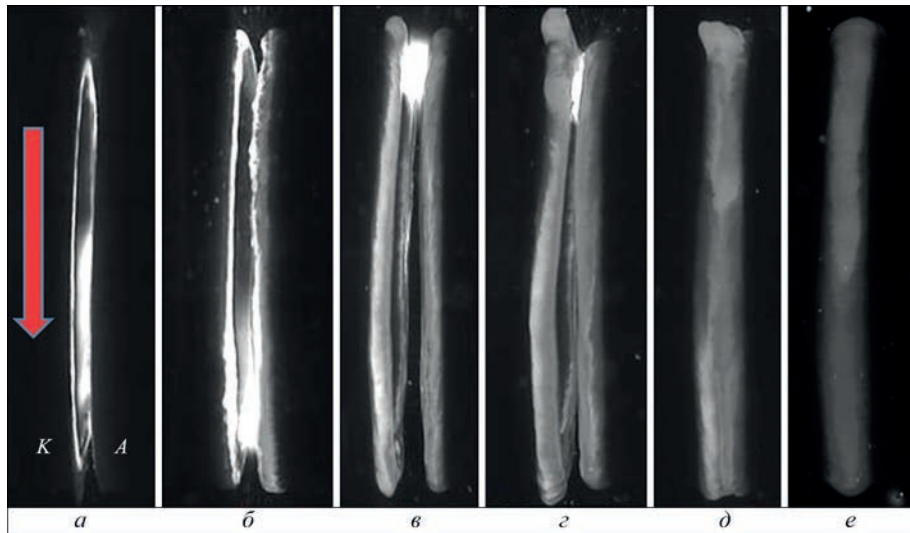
Стадії зварювання труб: а – початок переміщення дуги під дією КМП; б – формування шару розплаву на торцях труб; в – переміщення розплаву в процесі нагрівання; г – оновлення розплаву перед осадкою; д – початок осадки; е – формування зварного з'єднання
